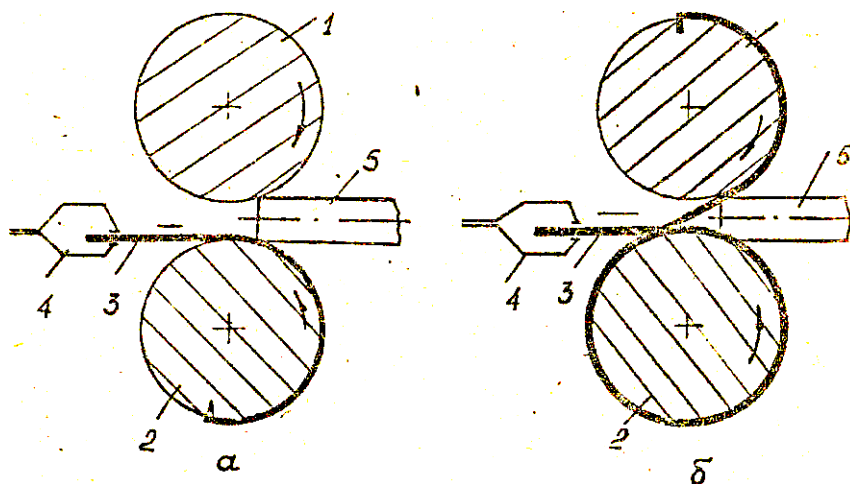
Вариант выполнения привода роликовой волоки с гибкой связью: 1 и 2 - ролики; 3 - гибкая связь; 4-тянущий орган стана; 5 - заготовка; а - связь охватывает один ролик; б - два ролика
